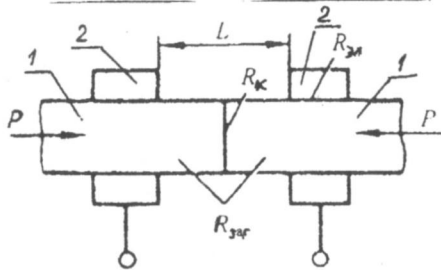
Схема контактной сварки: 1 – заготовки;
